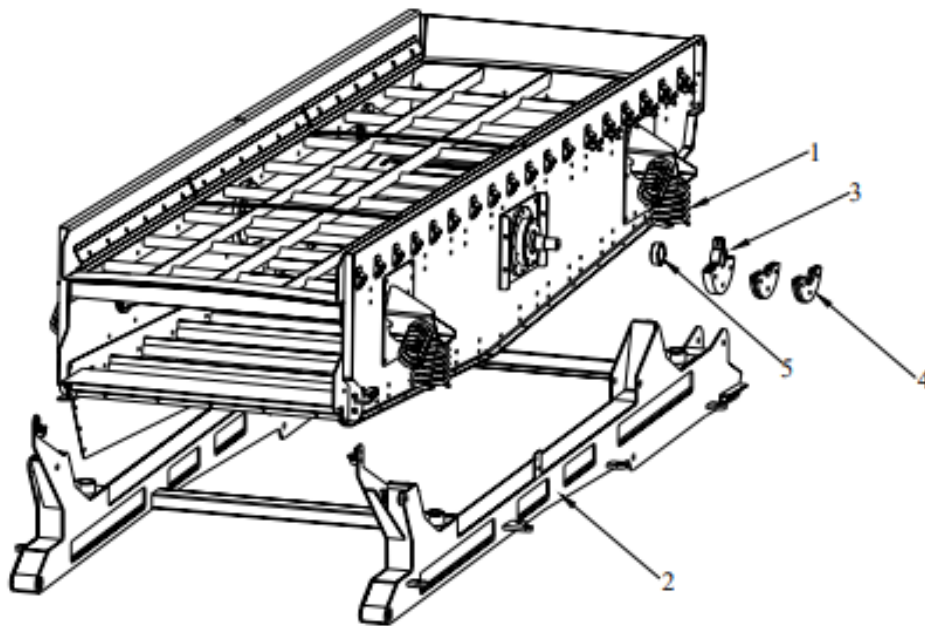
Unidad de tamizado del equipo de cribado Fintec 542 (1. muelles (x8), 2. Marco, 3. volantes , 4. accesorios de ajuste, 5. rodamientos (x2) (Crusherworks.com, 2011)
